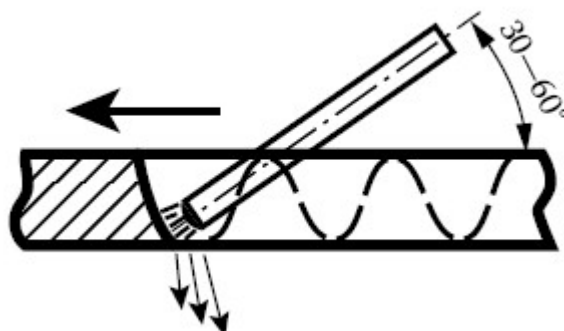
Схема ручной дуговой резки металла плавящимся электродом
